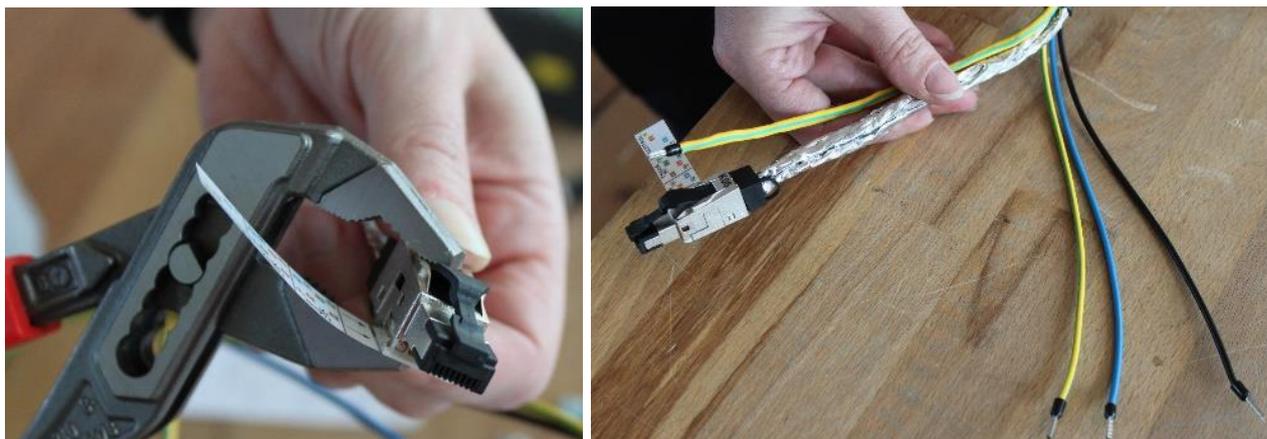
Fertige Verbindung mit dem Stecker
